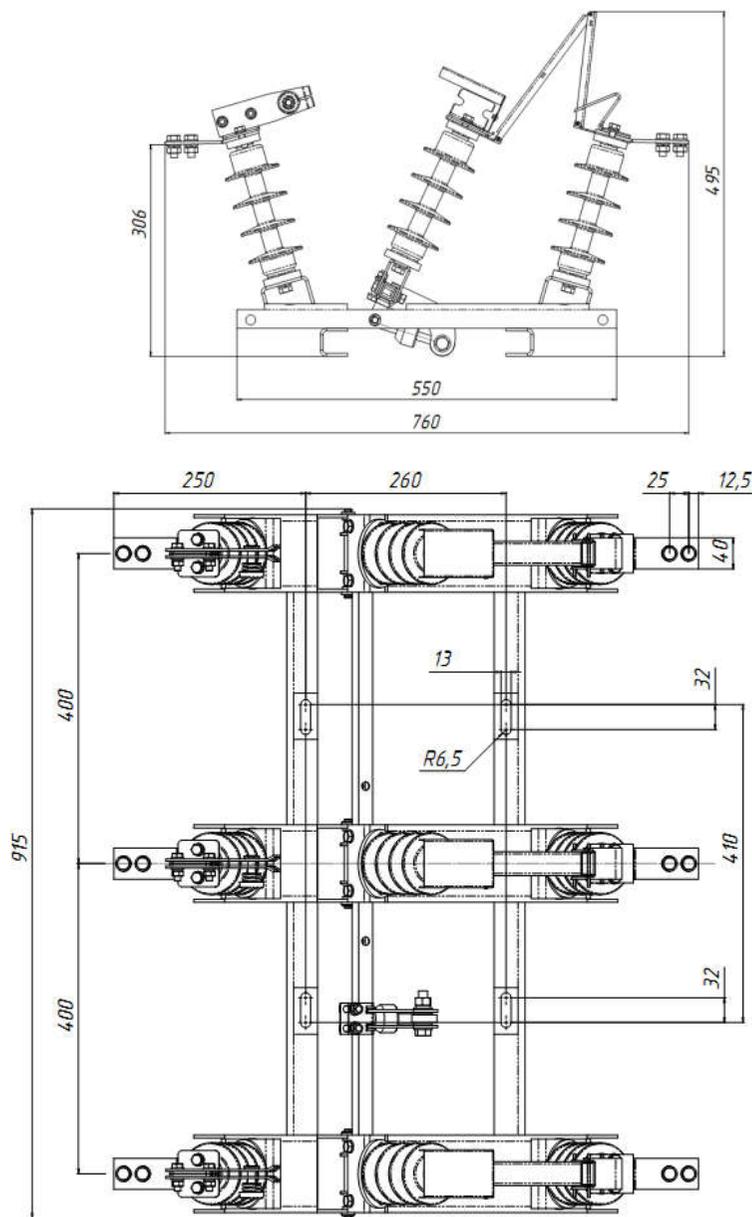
Б Разъединитель РЛК-II-10I400 –УХЛ1
